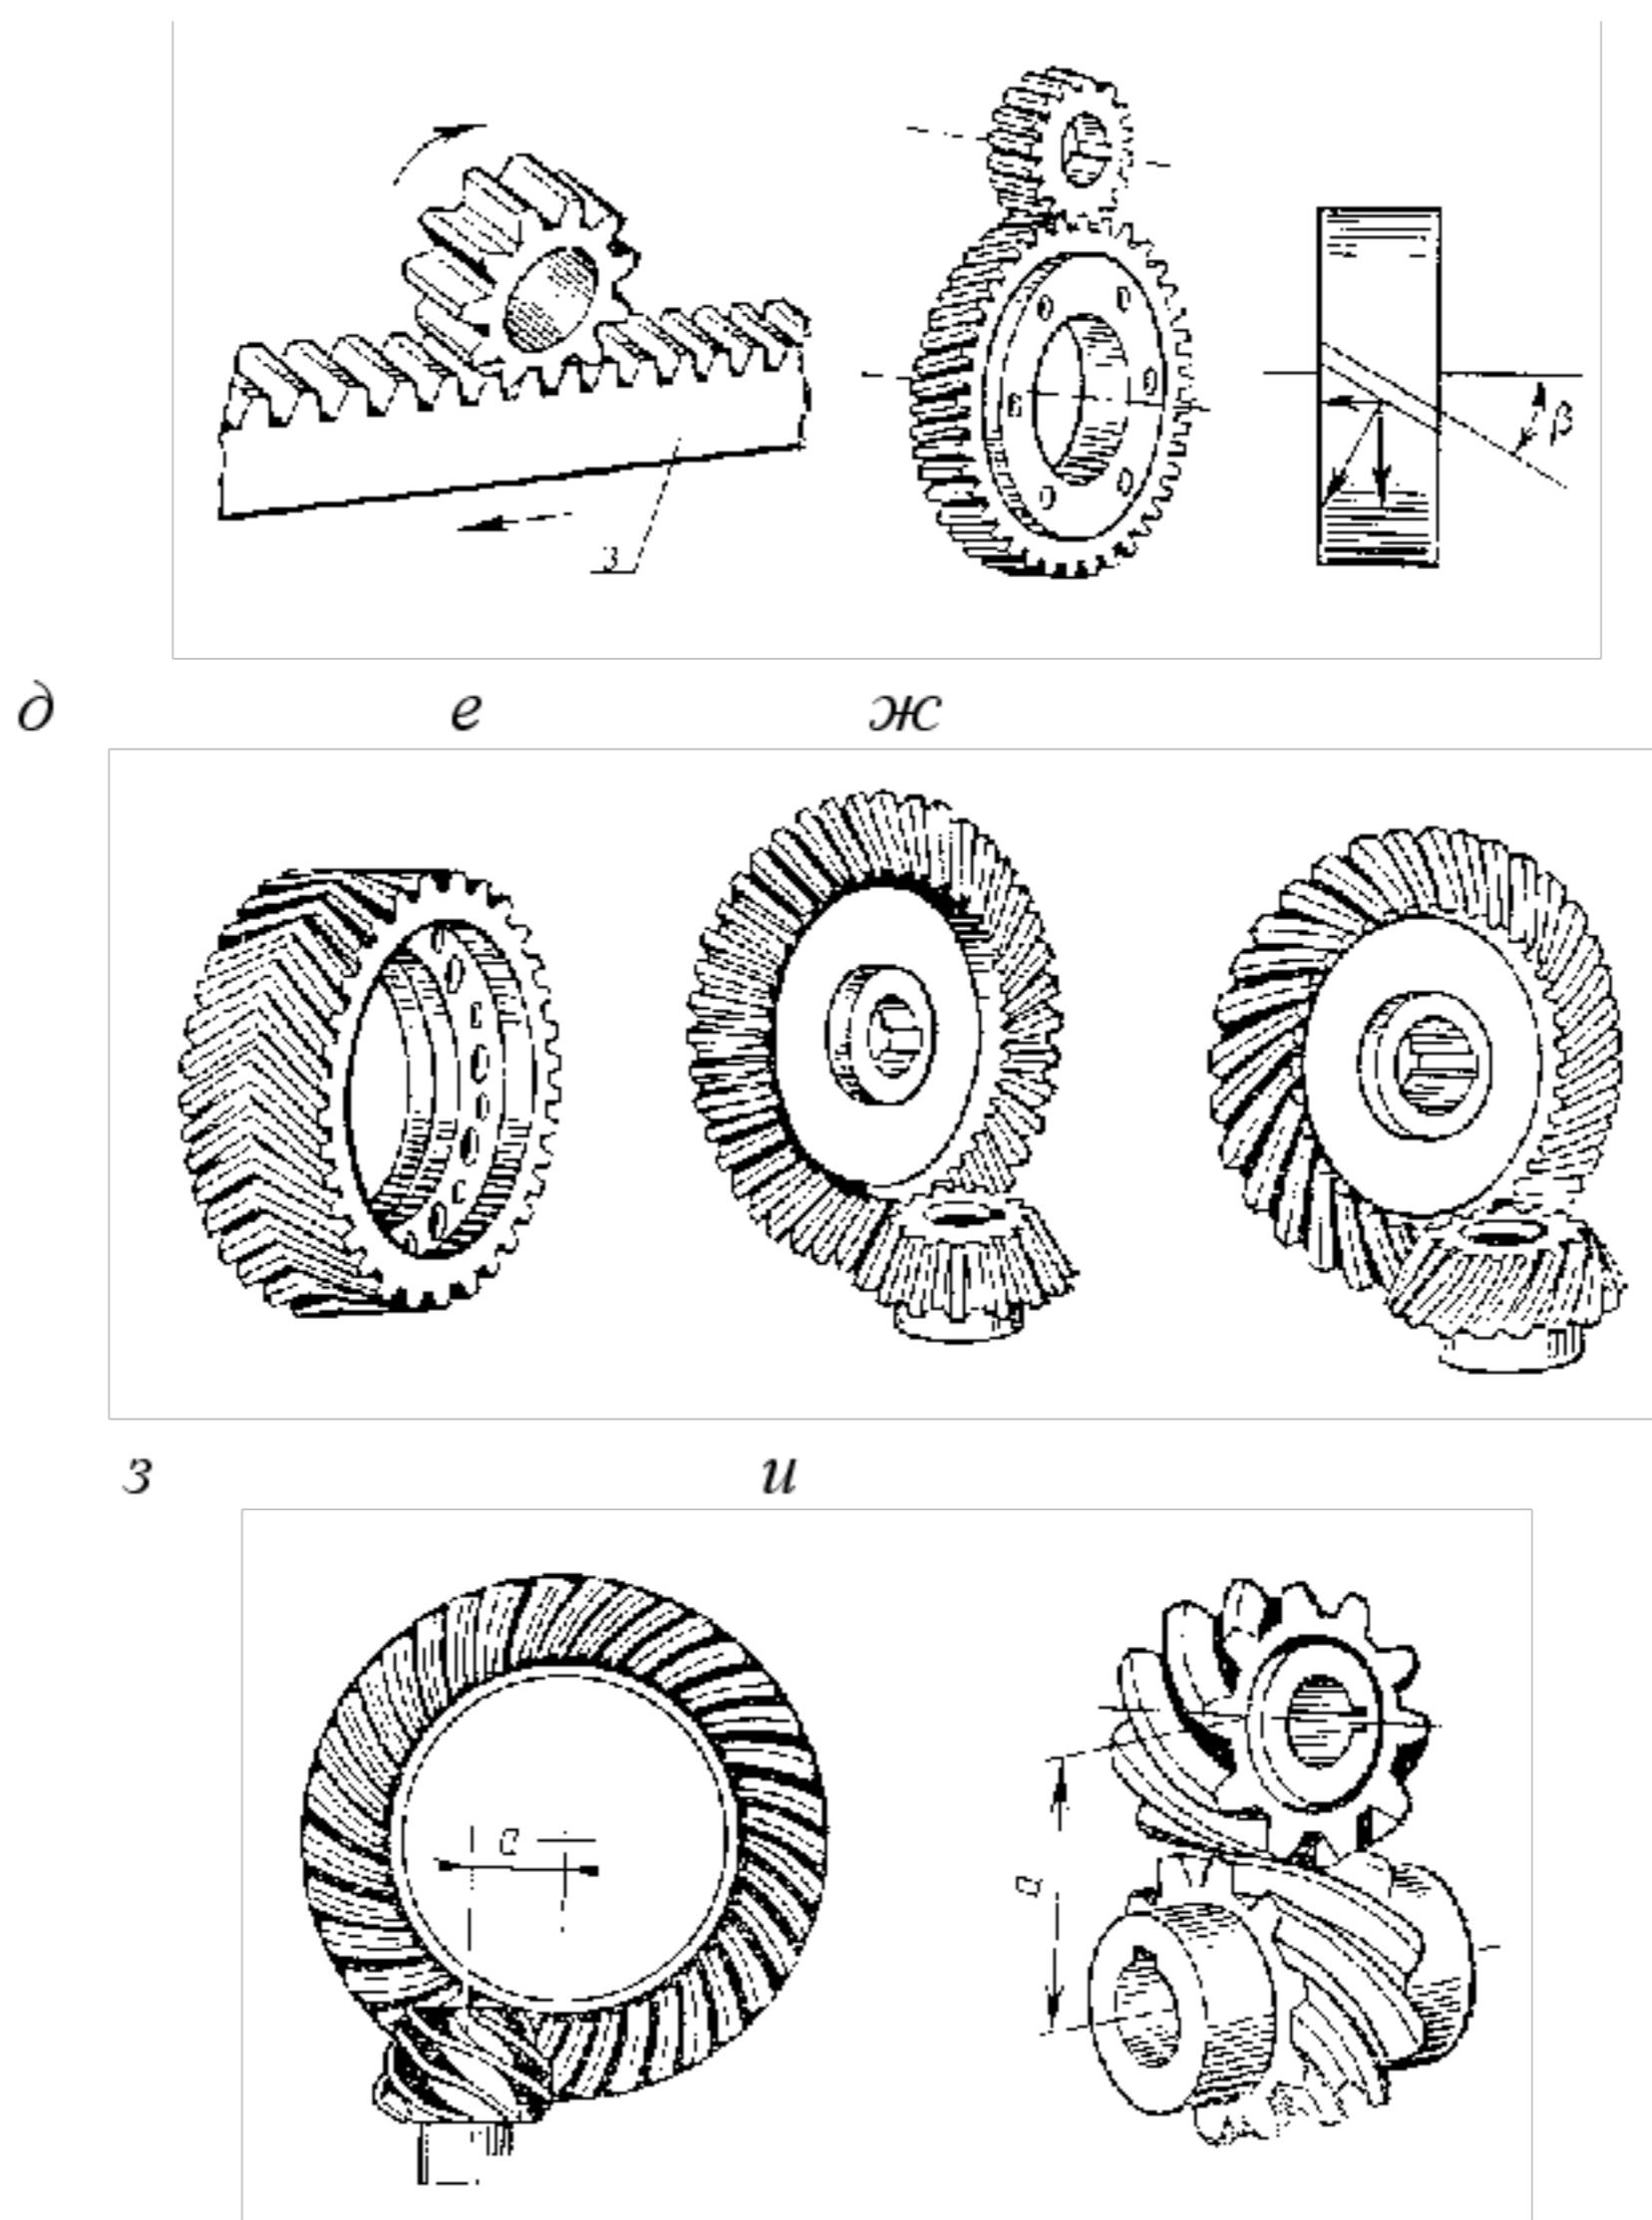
Виды зубчатых передач: 1 – шестерная; 2 – колесо; 3 – рейка
